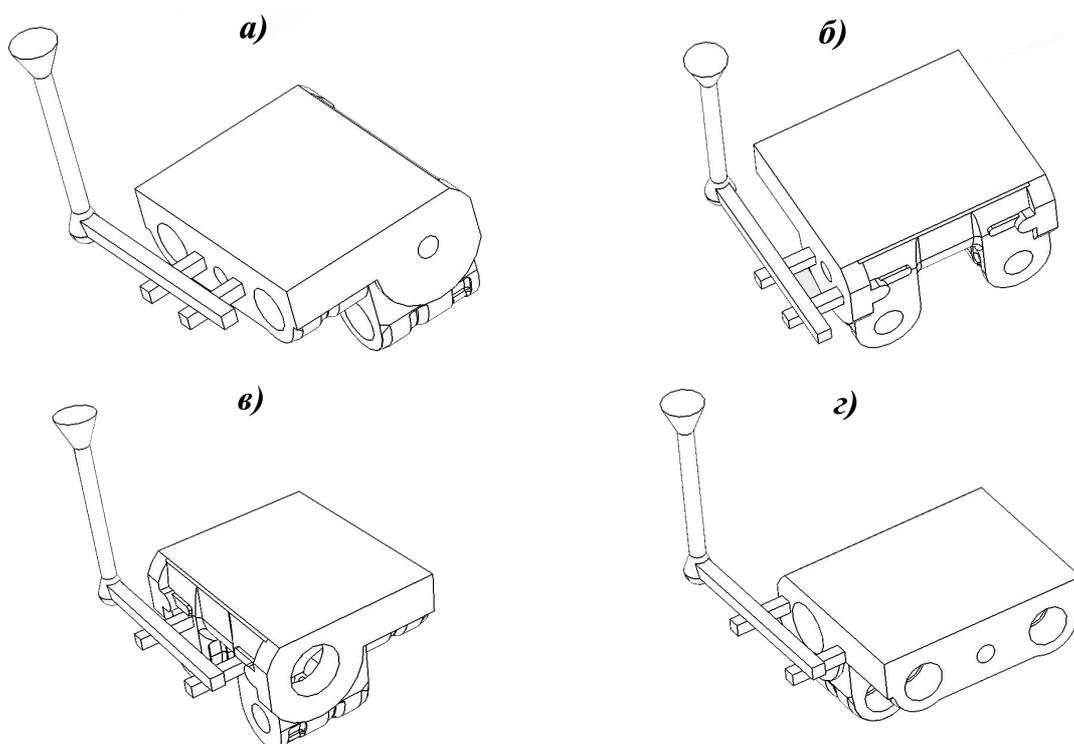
Схемы подвода металла к отливке: а – подвод спереди; б – подвод с правого бока; в – подвод сзади; г – подвод с левого бока
